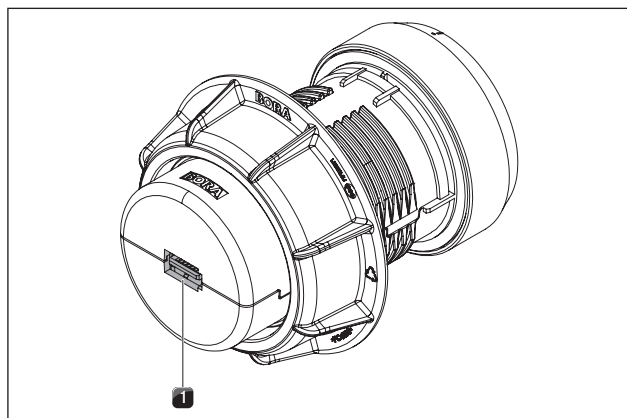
Tilslutning til betjeningsknappen, bagside
